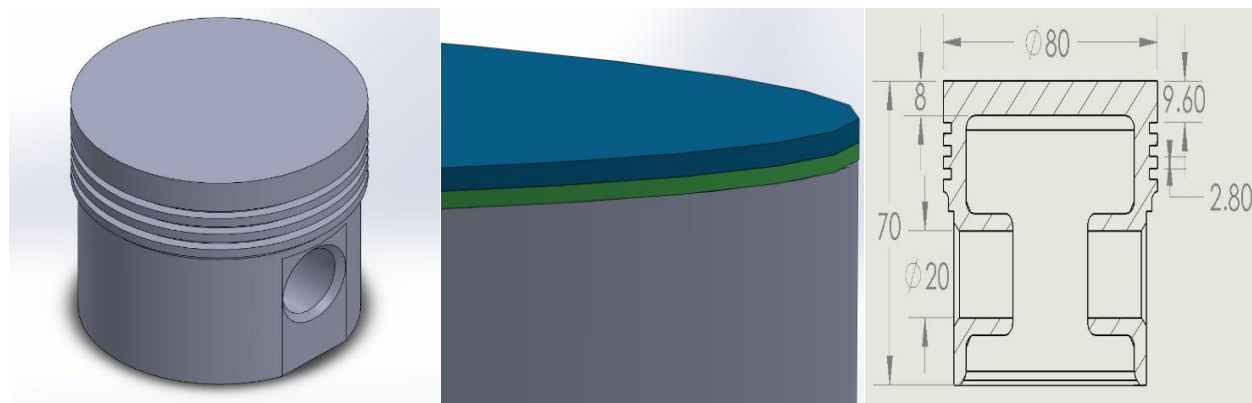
a) Geometría Pistón b) material cerámico y capa de enlace c) Vista sección de Pistón
